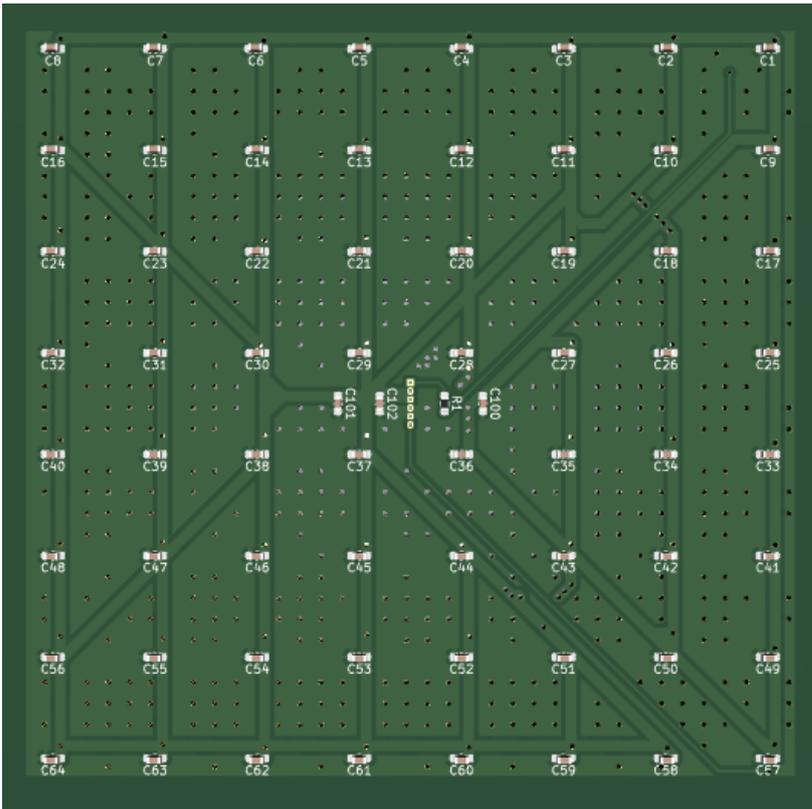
cara de soldadura de PCB submódulo_leds. (Creación propia)
